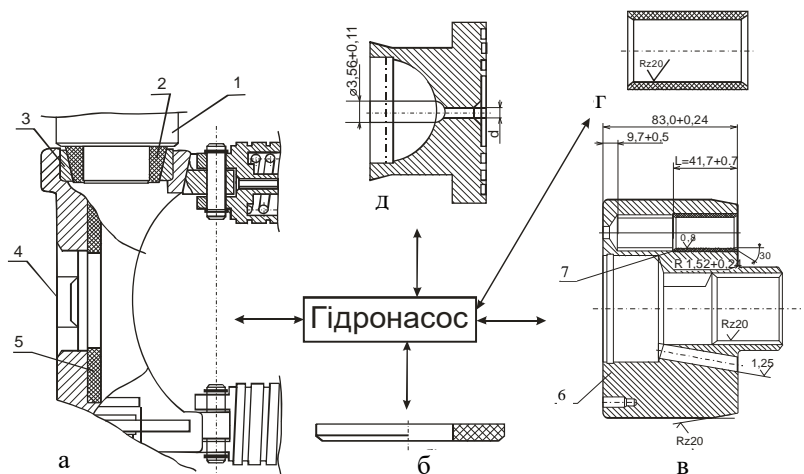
Напрями удосконалення гідронасоса: а – люлька насоса; б – опорна пластина люльки; в – блок циліндрів з втулкаим; г – індивідуальна композитна втулка блока циліндрів; д – сталева п'ята плунжера блока циліндрів; 1 – цапфа; 2 – композитна втулка підшипника; 3 – сталева втулка підшипника; 4 – люлька; 5 – опорна пластина люльки; 6 – блок; 7 – композитна втулка
